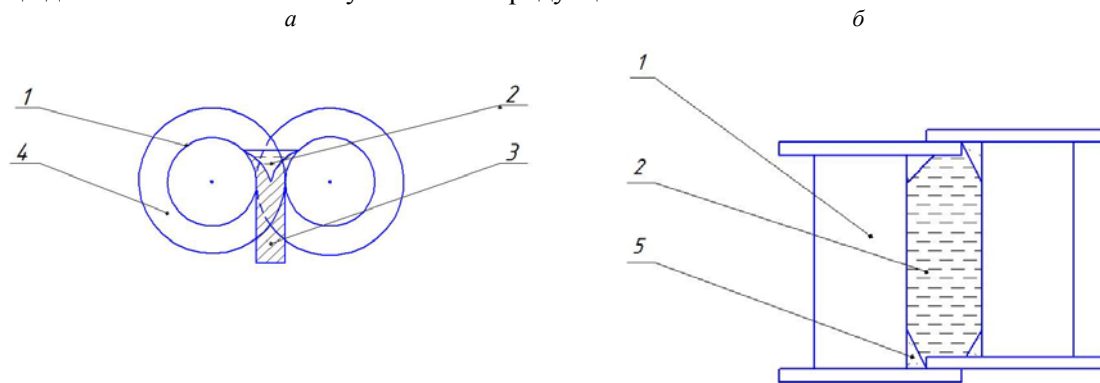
Ливарно-прокатна кліть [14]: *а* - вигляд збоку; *б* - вигляд зверху;
